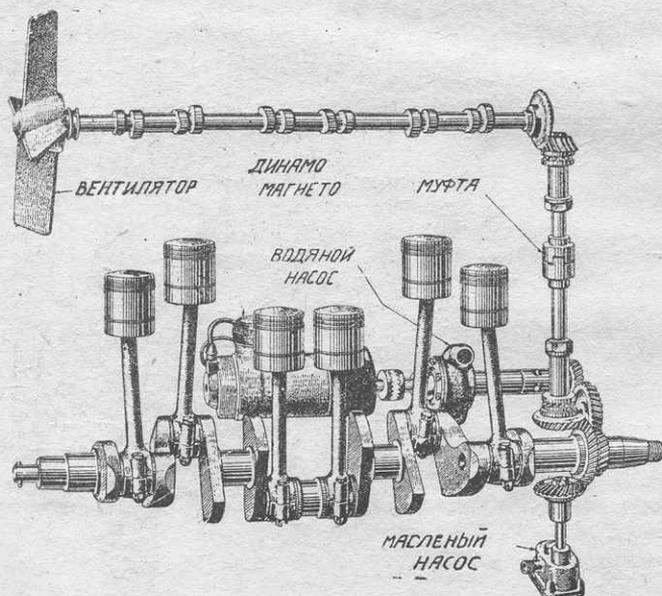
Схема привода верхнего кулачкового валика шестицилиндрового двигателя с прилегающими деталями двигателя.
